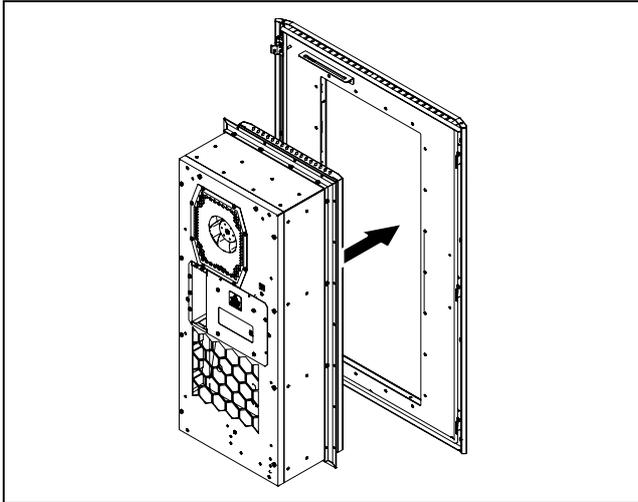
Montaje del refrigerador en una pieza plana de pared doble
